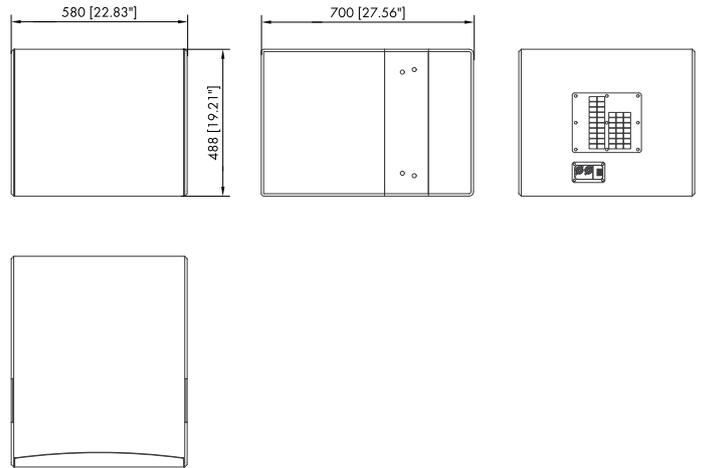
27A-SUB Gehäuseabmessungen in mm [Zoll]
